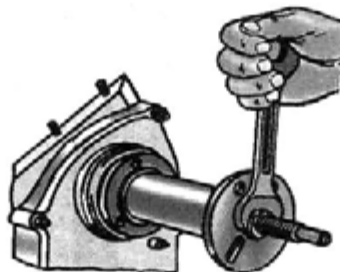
Напрессовка ступицы шкива коленчатого вала с помощью приспособления 16-У-236817
